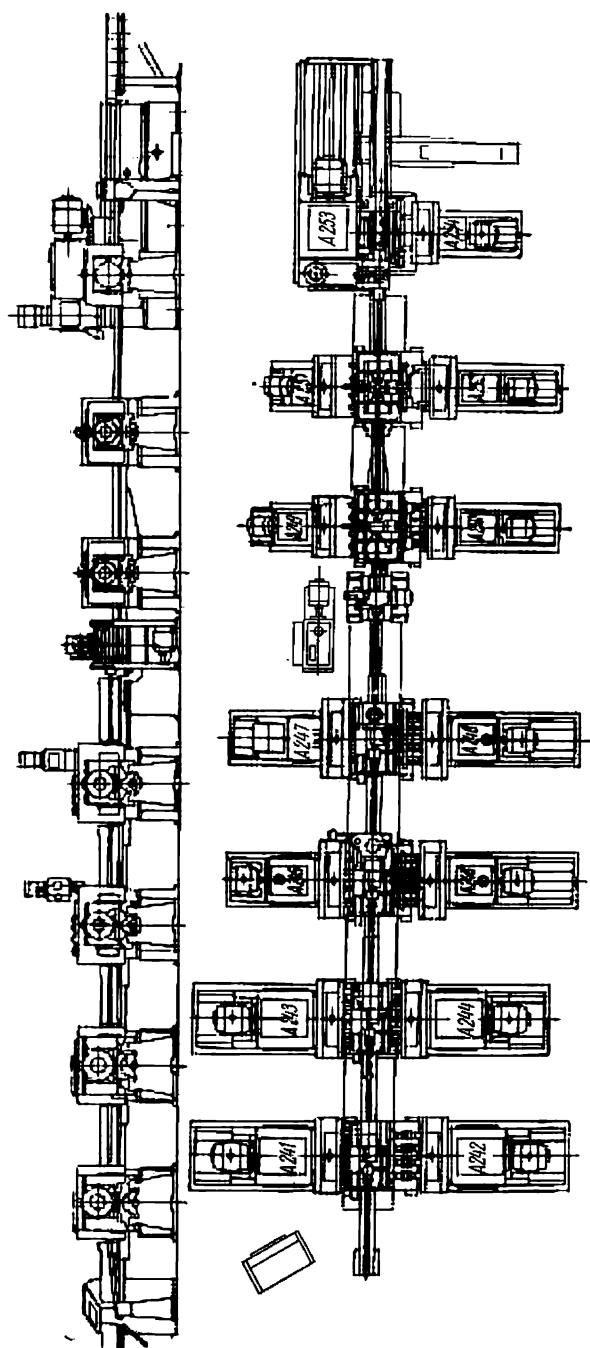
Circuit de machines transfert pour l'usinage du bloc cylindres d'un camion
